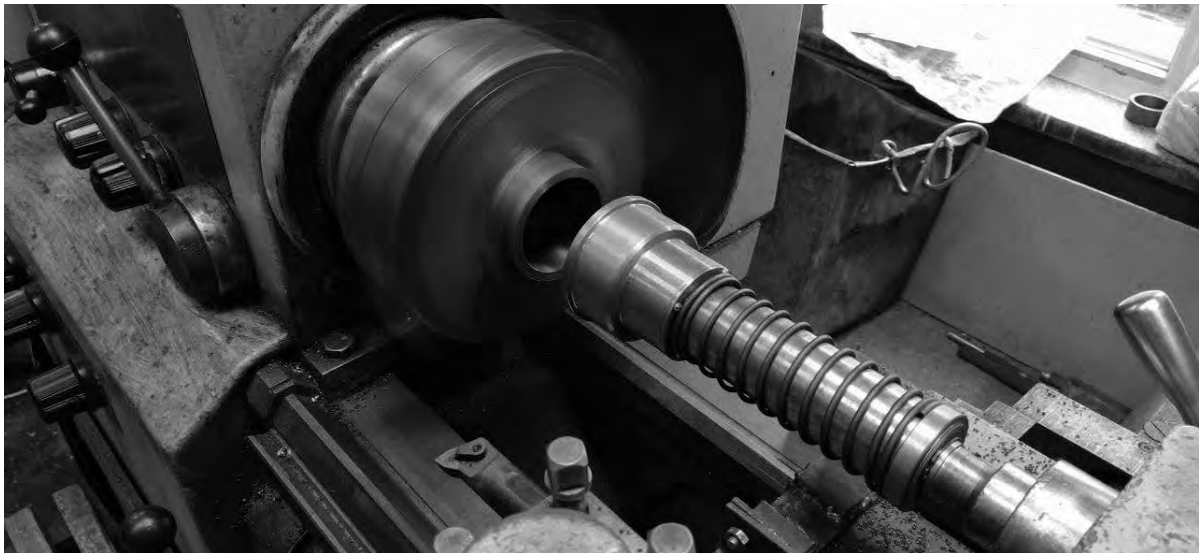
ИИО заготовки на станке 16К20ПФ1
